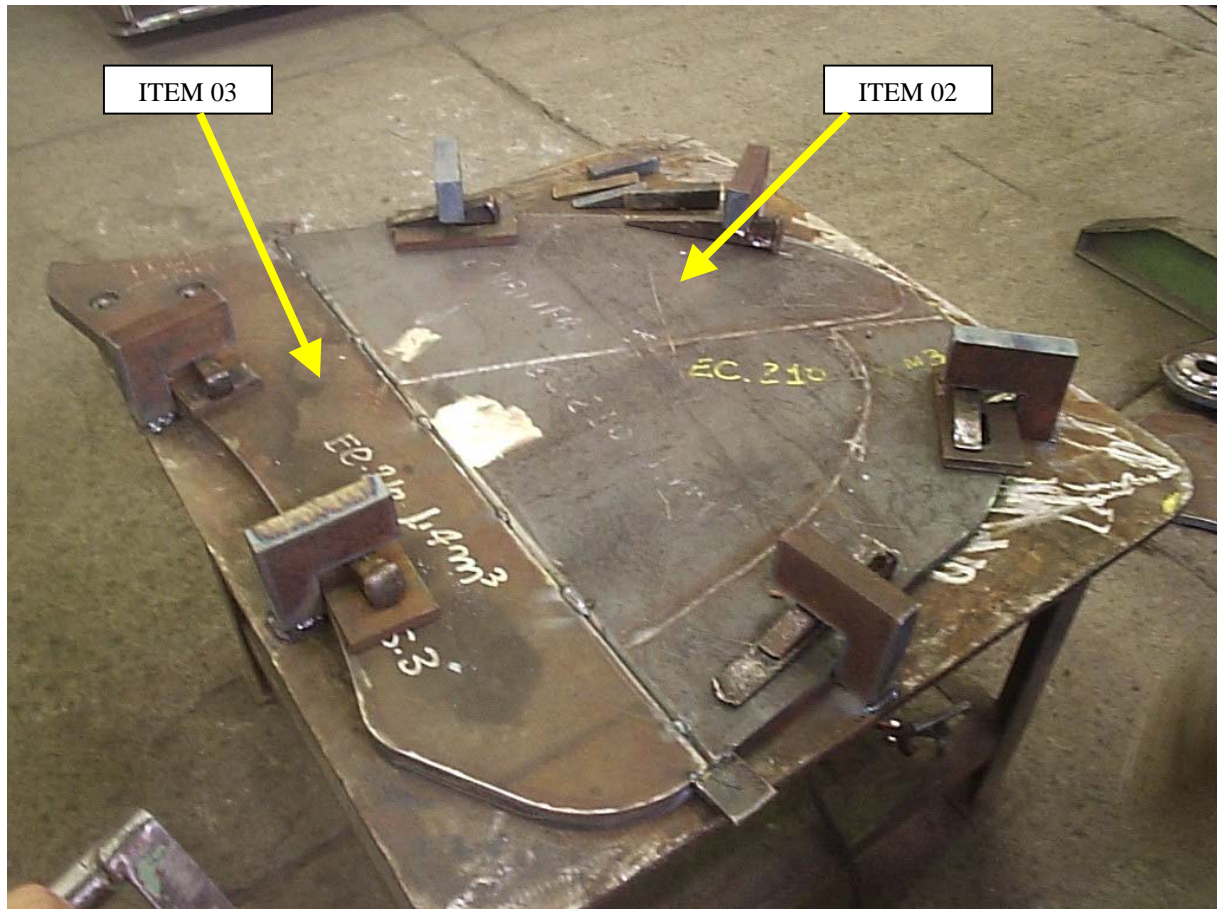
Mesa de fixação para a soldagem do SC06
